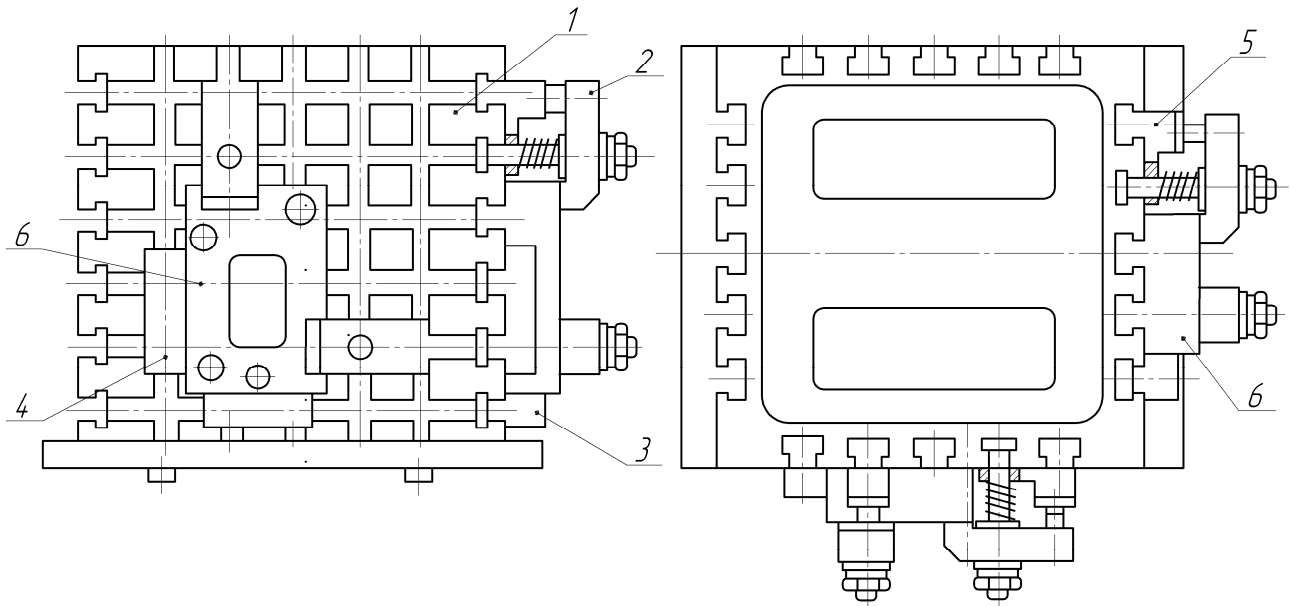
Будова чотирибічного косинця в робочому положенні: 1 – косинець; 2 – прихоплювачі (ГОСТ 4735-69); 3, 4 – упор; 5 – опора; 6 – заготівка
